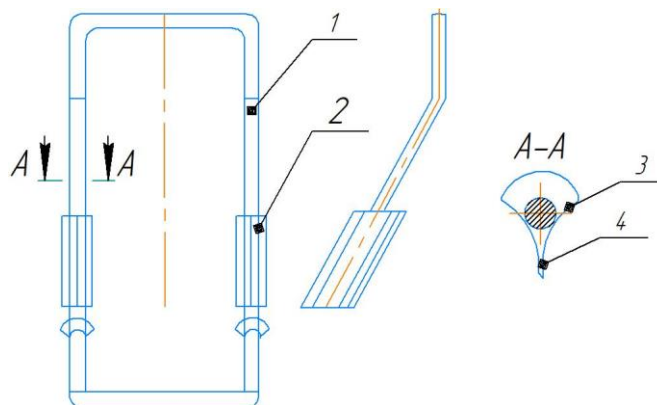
Удосконалений загортач зернової сіялки: 1 – стійка, 2 – робоча поверхня, 3 – лезо, 4 – напрямна.
